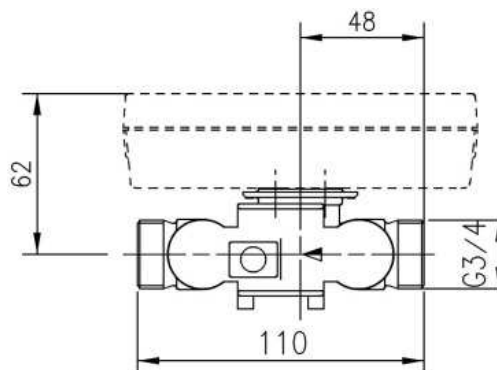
Översikt dimensioner total längd 110 mm (gängad)
